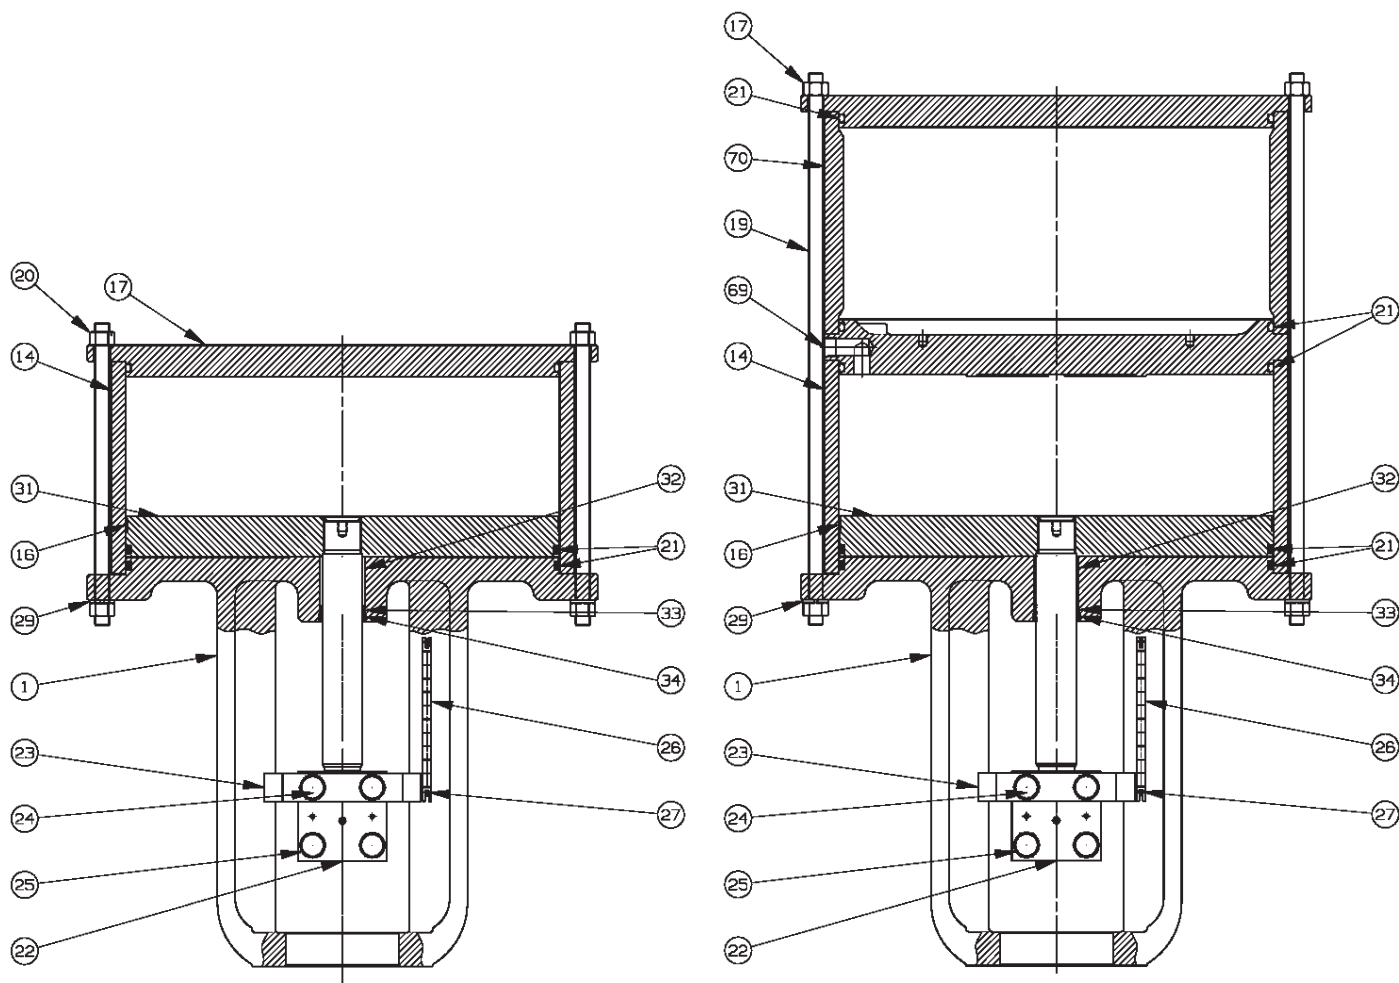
Модель 51 без маховика, с резервуаром для сжатого воздуха и без резервуара
